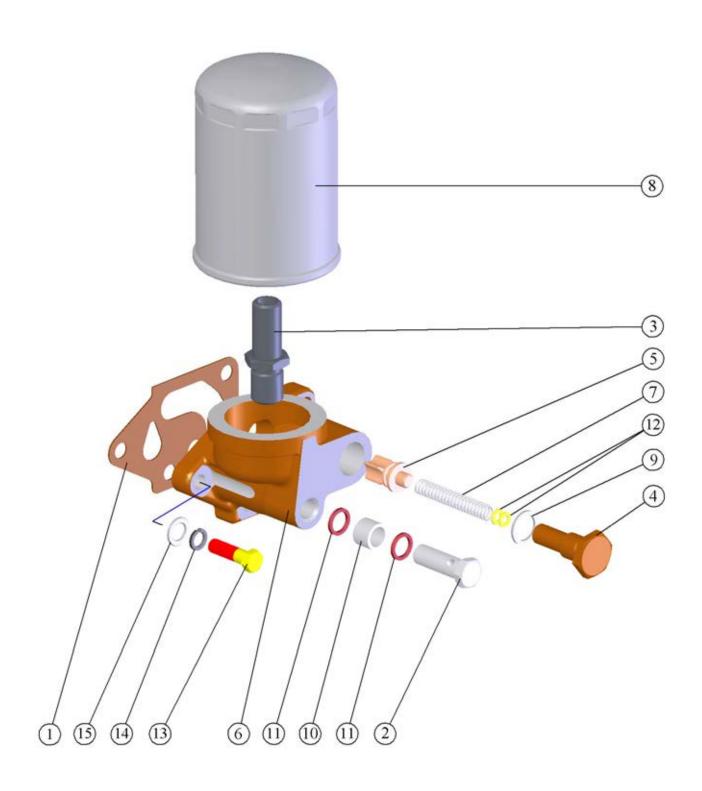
Установка фильтра очистки масла. Fig. 17 Oil filter installation.
